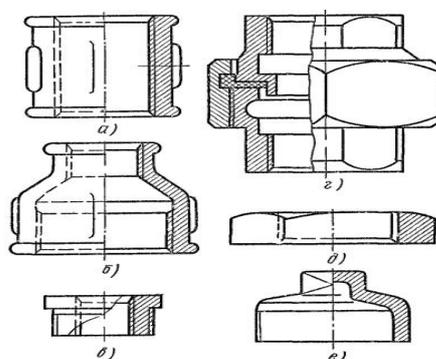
Соединительные части из ковкого чугуна для сборки труб по прямой:
